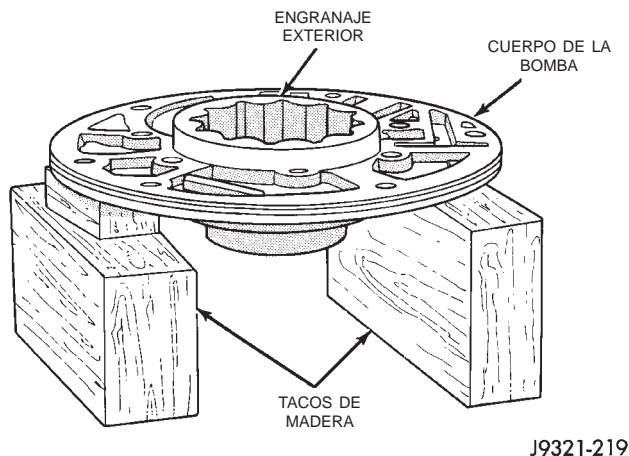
Sujeción de la bomba e instalación del engranaje exterior
